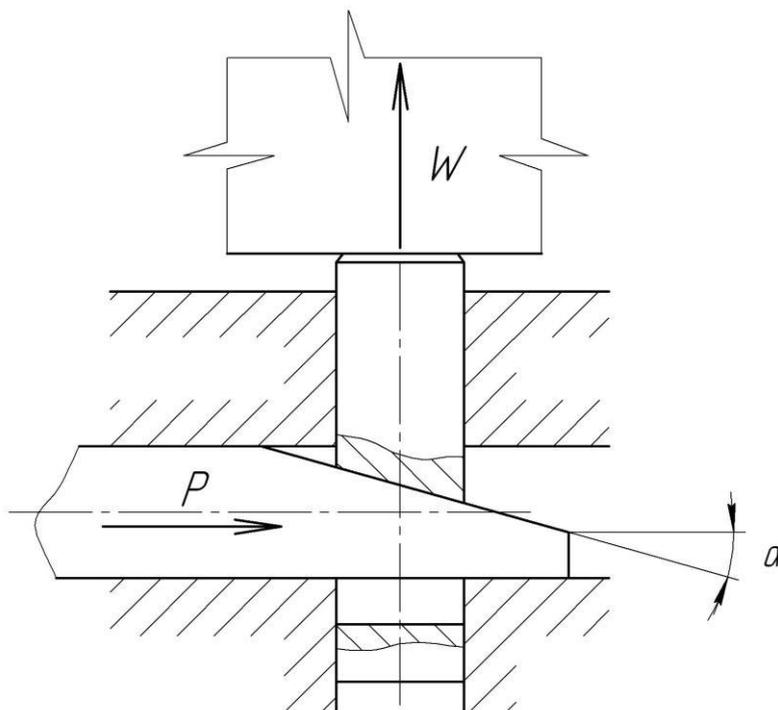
Двухопорный клиноплунжерный зажимной механизм
